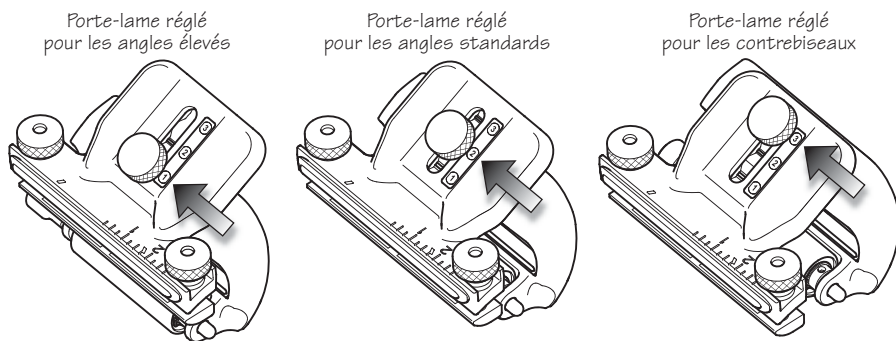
Réglage du porte-lame pour chaque type de biseau
